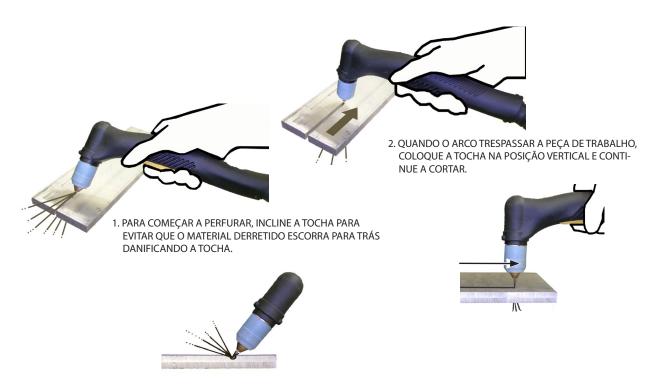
Técnicas de perfuração e corte utilizando a PT-38
